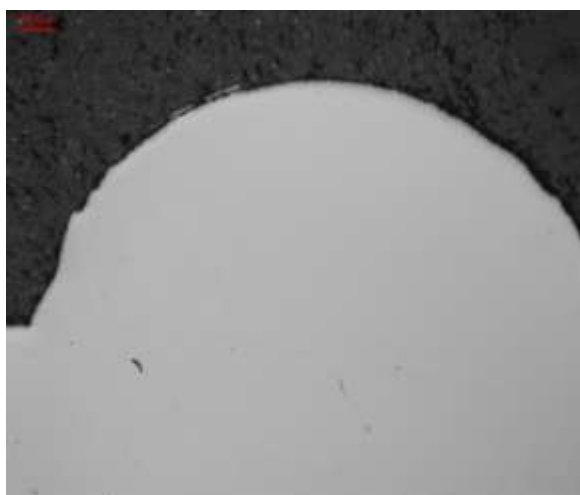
Вид наплавочного валика штамповой стали после лазерной наплавки
